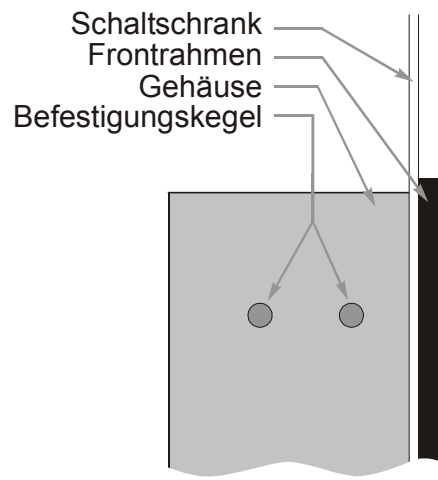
Seitenansicht - ohne Befestigungsklammer
